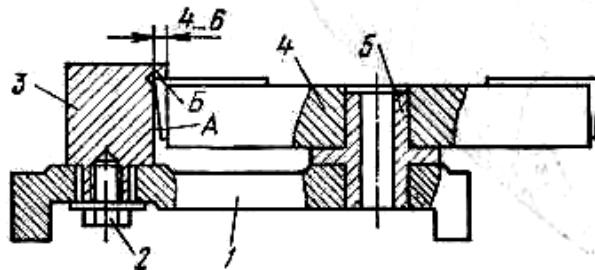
Контрольно-установочное приспособление для настройки шипорезных фрез: 1 – плита, 2 – болт, 3 – упор, 4 – фреза
